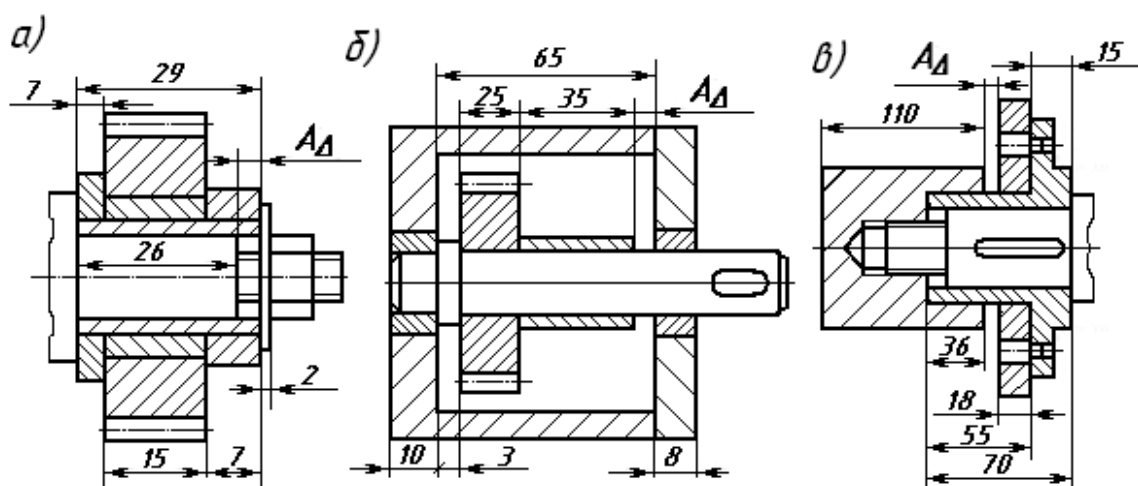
Эскизы сборочных единиц для расчета размерных цепей
